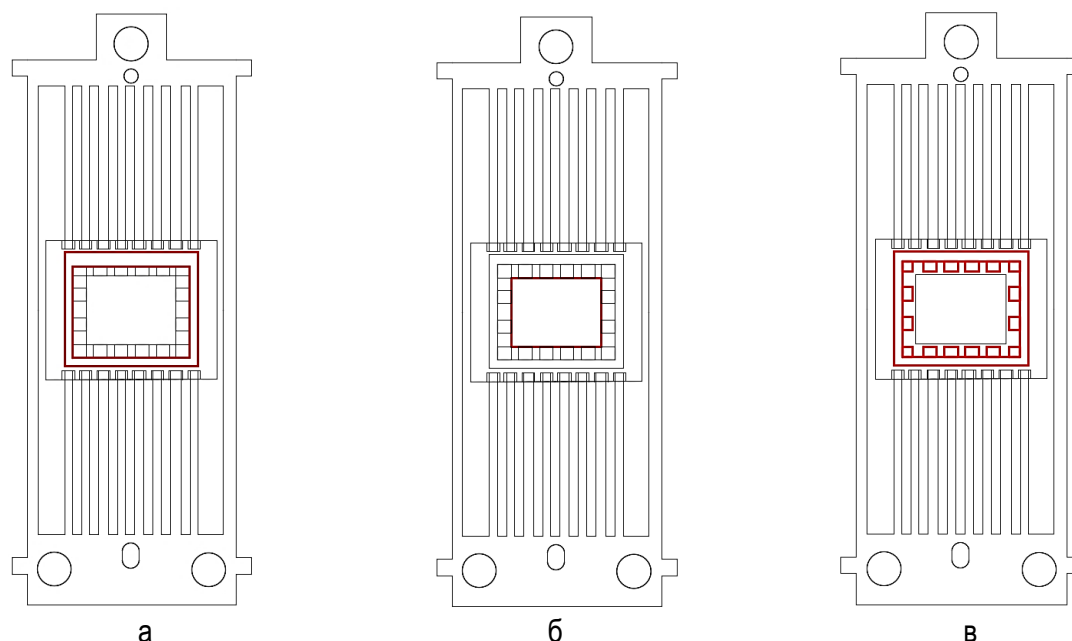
Виды некачественных корпусов: а) некачественная заливка корпуса; б) выпуклая площадка для монтажа; в) отличия в цвете контактных площадок и керамической части корпуса
